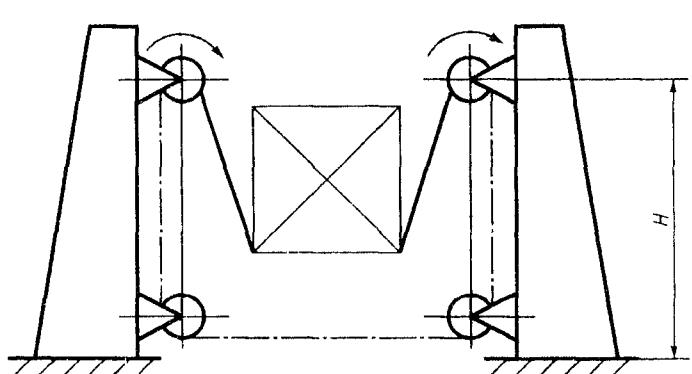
Кантователь цепной с четырьмя звездочками
